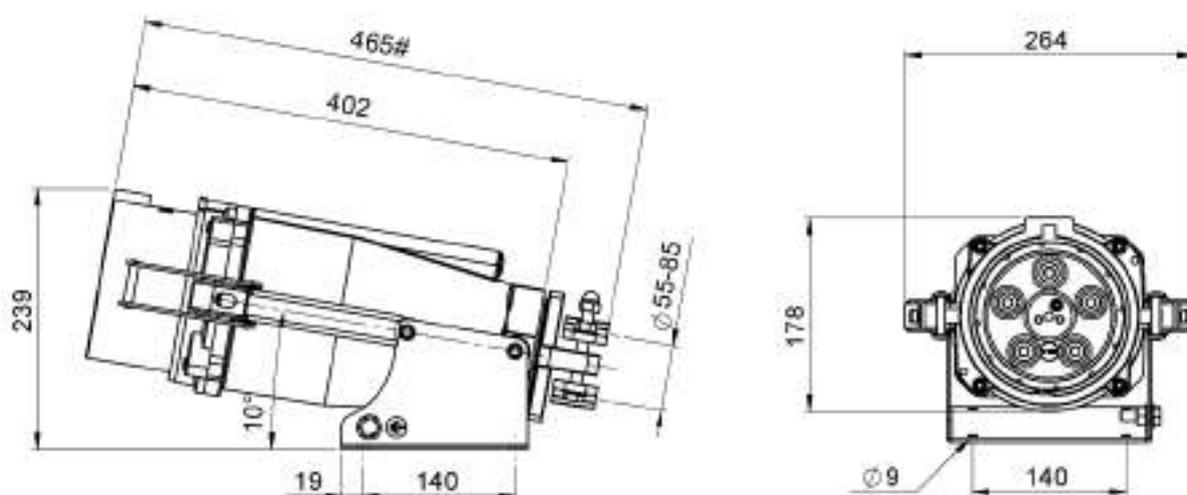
Abmessungen Gerätestecker MCW A-Line (500 A – 600 A) in mm
